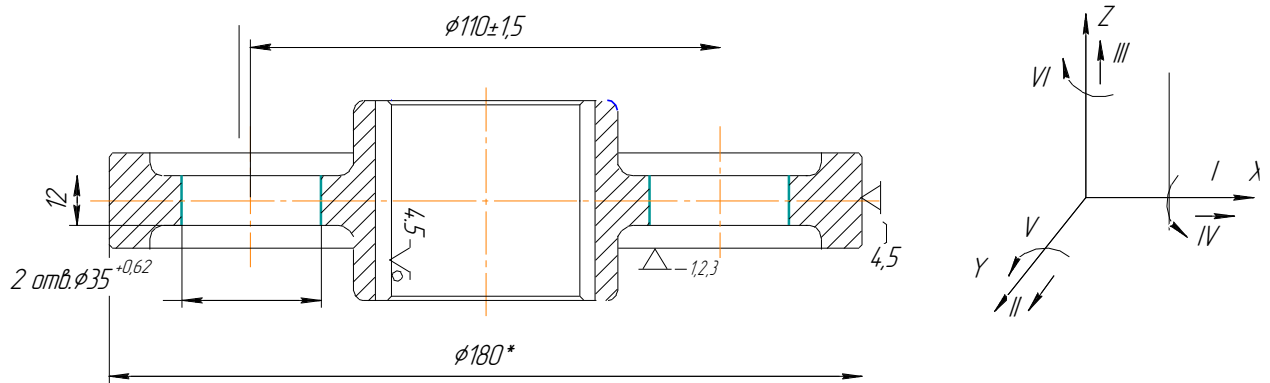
Схема базування заготовки по отвору і торцю
